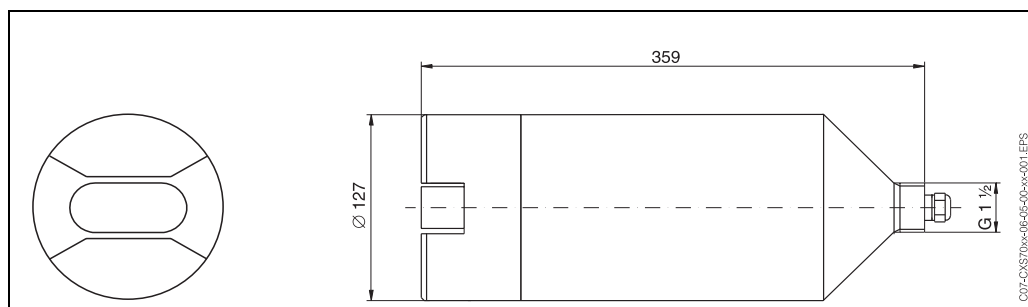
Dimensions du capteur CNS 70 et vue d'en haut de la surface de mesure.
